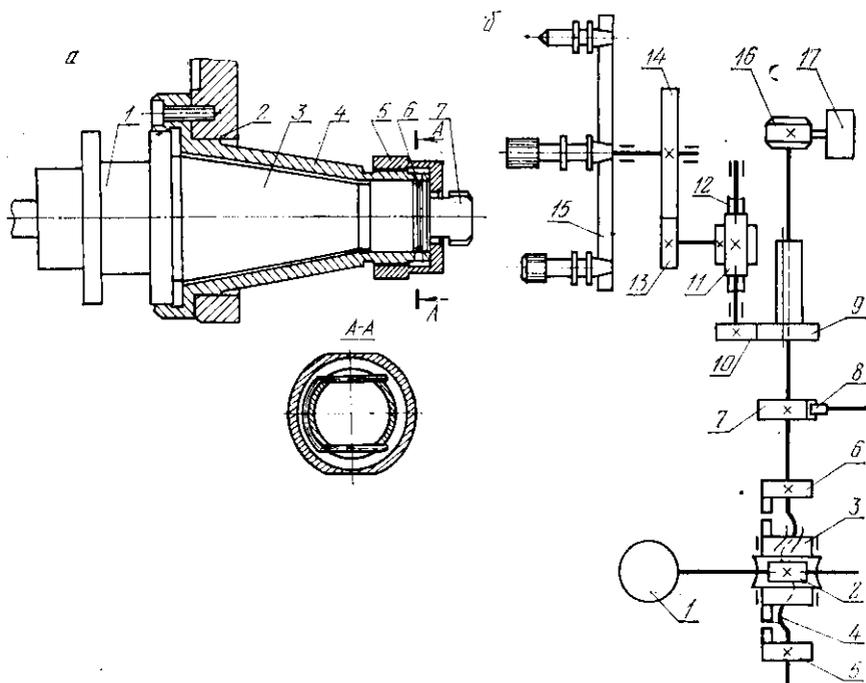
Инструментальный магазин станка 243ВМФ4
